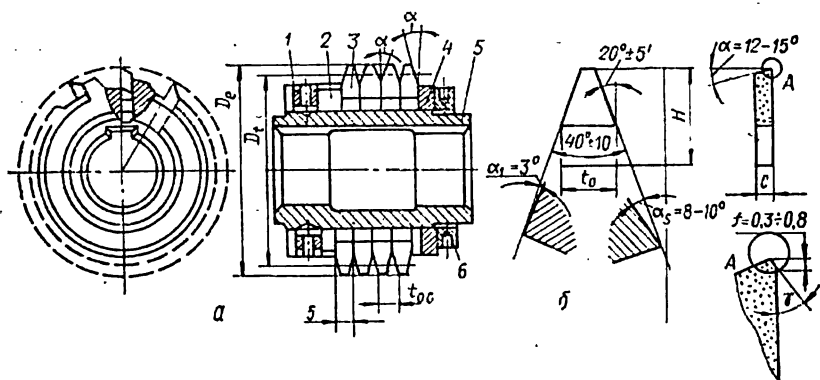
Твердосплавная червячная модульная фреза (а) и геометрические параметры ее режущей части (б).
